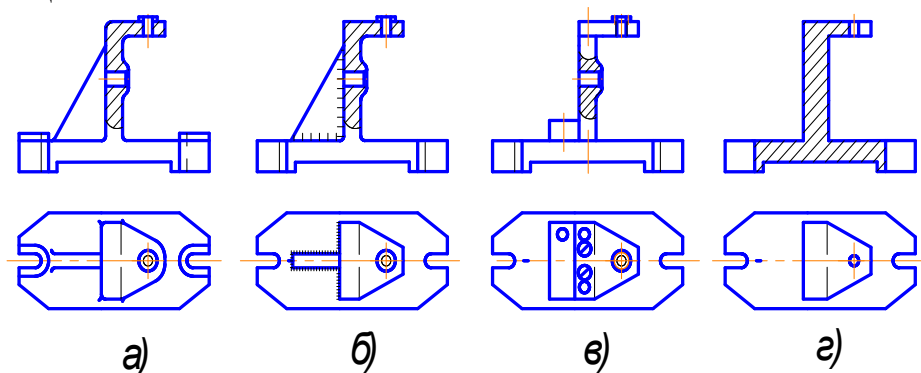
Варианты выполнения корпуса: а) литого; б) сварного; в) сборного; г) кованного
